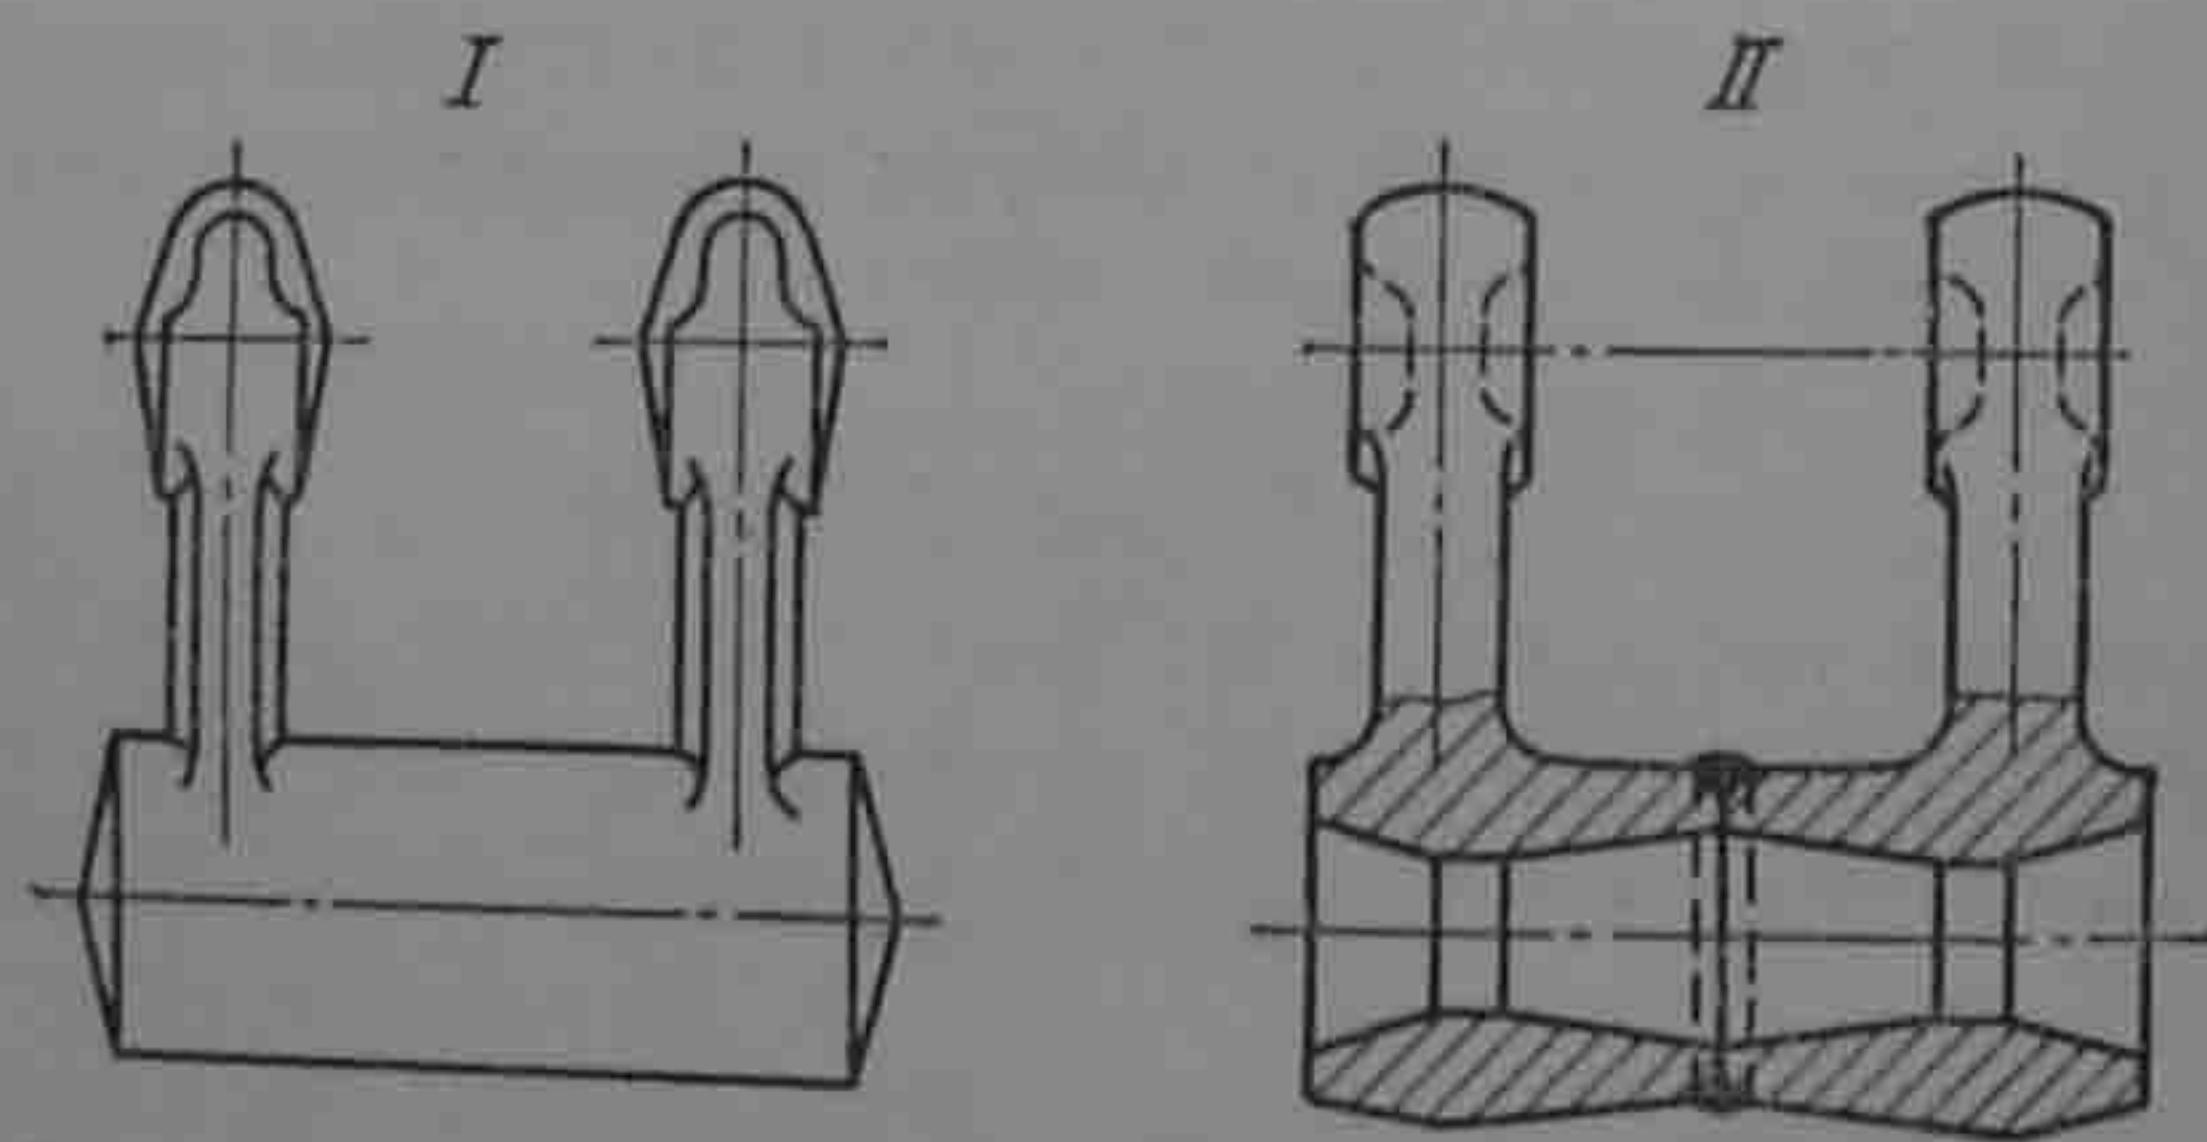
Упрощение способа штамповки путем последующей сварки отдельных частей поковки
